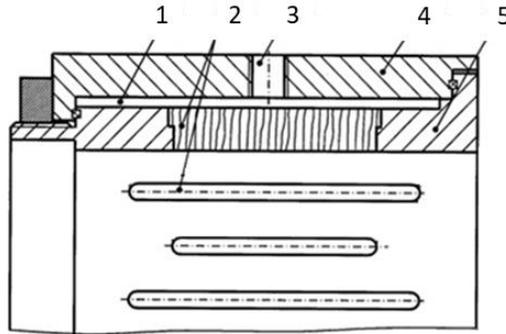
Газостатический подшипник (1 - камера, 2 - пористые вставки, 3 – подводящая магистраль, 4 - корпус, 5 - газонепроницаемая втулка).
